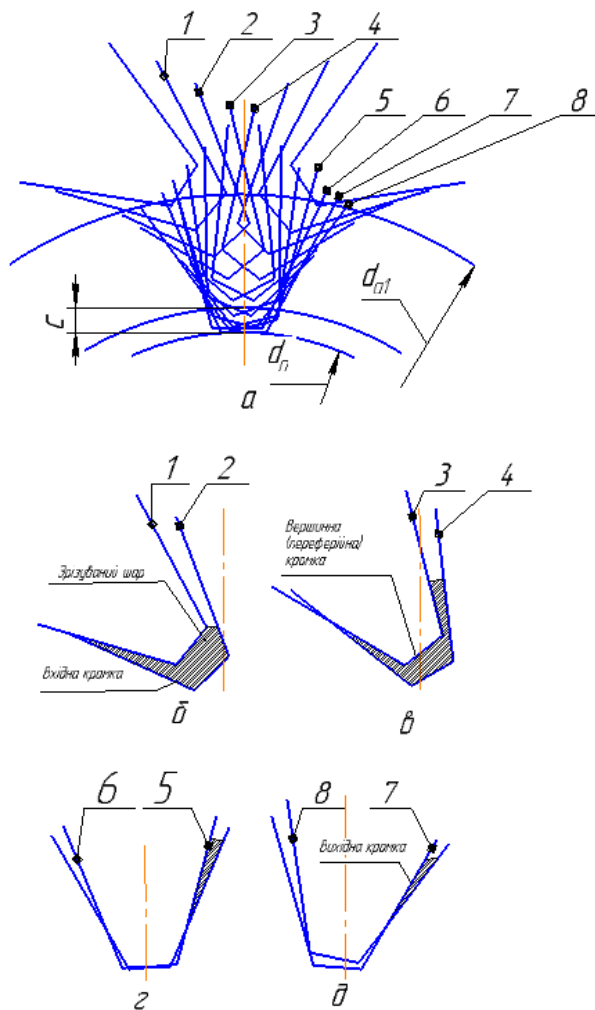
Схема утворення западини зуба колеса черв'ячною зуборізною фрезою із стандартним вихідним контуром за ГОСТ 13755-81.
